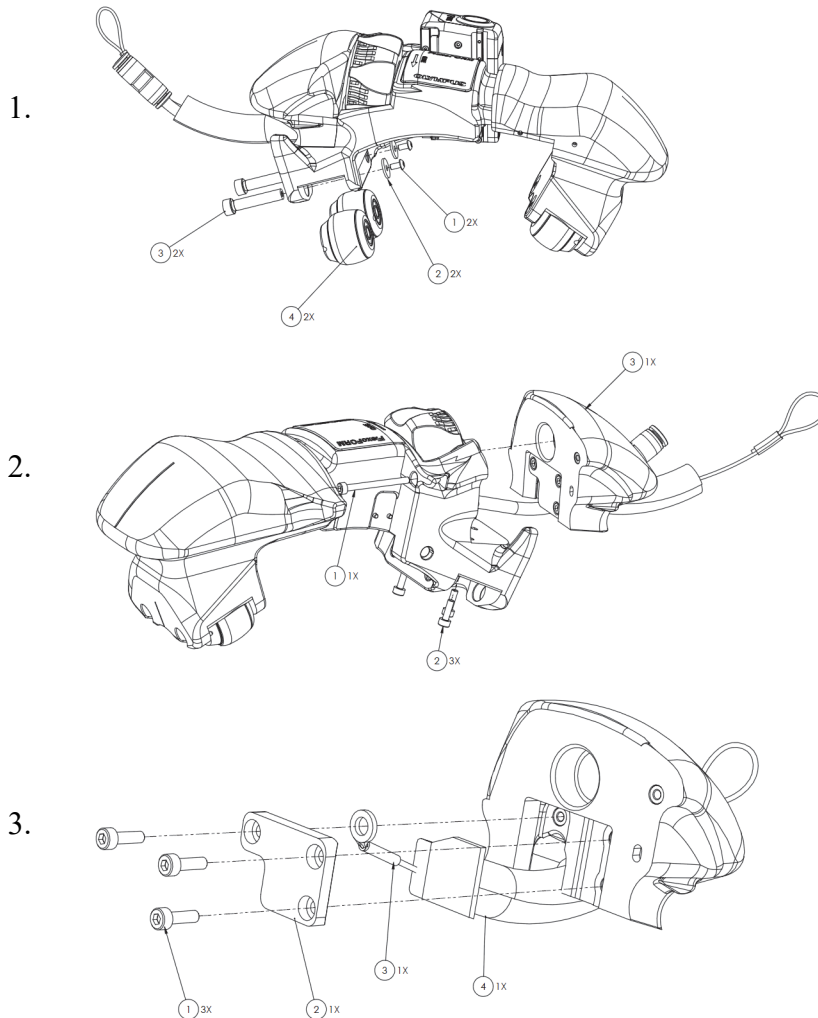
Operazioni di disassemblaggio per la sostituzione della guaina dei cavi
